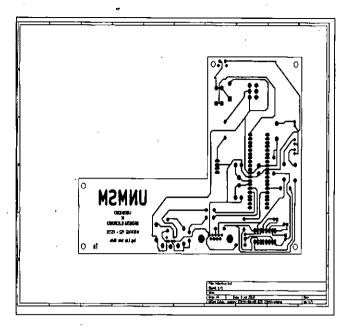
Diseño del PCB hecho con el Kicad
